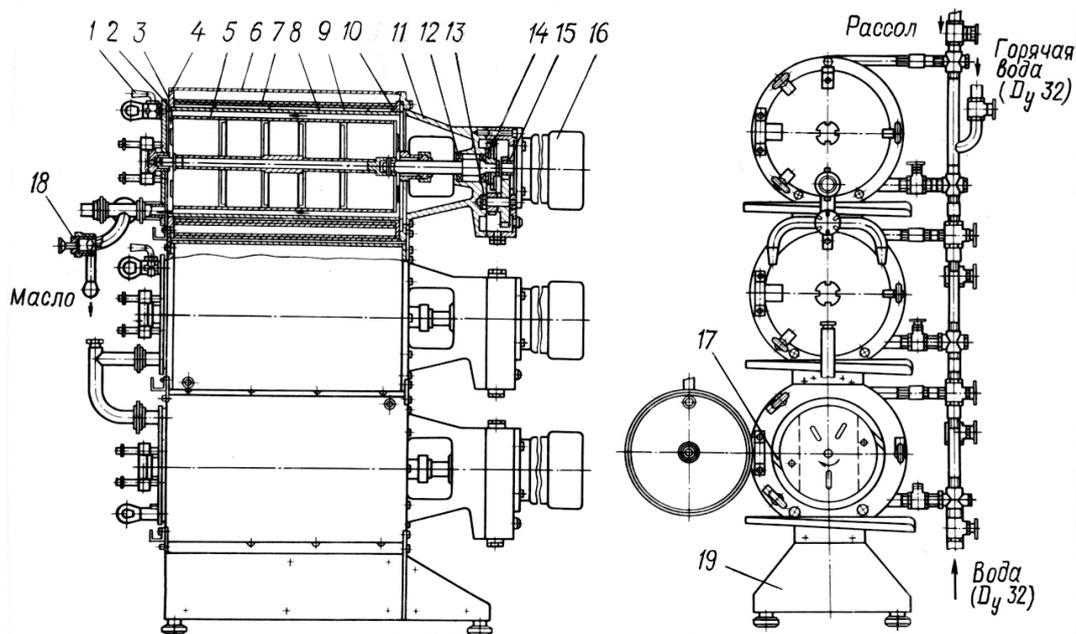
Маслообразователь трехцилиндровый: 1 – воздушный кран; 2 – крышка; 3 – уплотнительное кольцо; 4 – фланец; 5 – вытеснительный барабан; 6 – обшивка; 7 – наружная обечайка; 8 – спираль; 9 – внутренняя обечайка; 10 – задний фланец; 11 – редуктор; 12, 13 – подшипники; 14, 15 – шестерни; 16 – привод; 17 – ножи; 18 – выпускной кран; 19 – станина
